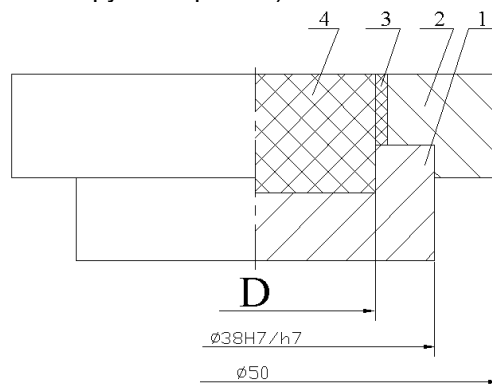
Форма для виготовлення зразків: 1 - корпус; 2 - кришка; 3 - пластмасове кільце; 4 - метало-полімер
